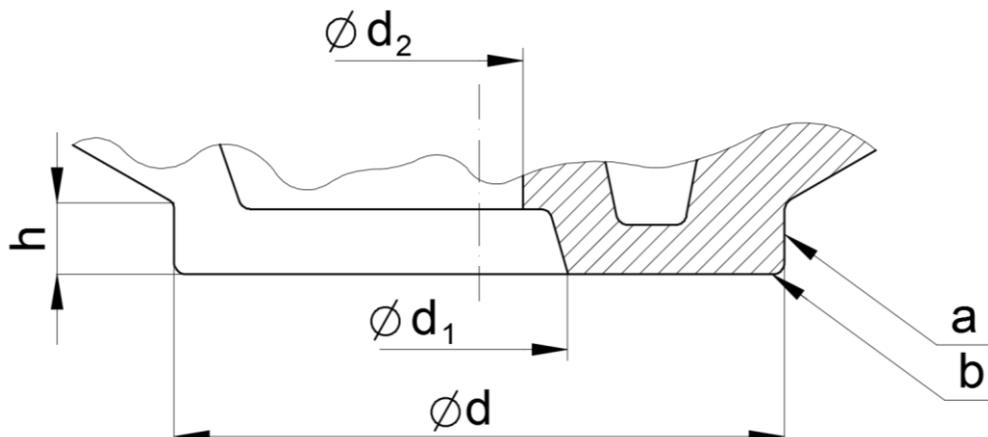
Присоединительные размеры пятника или пятникового места
